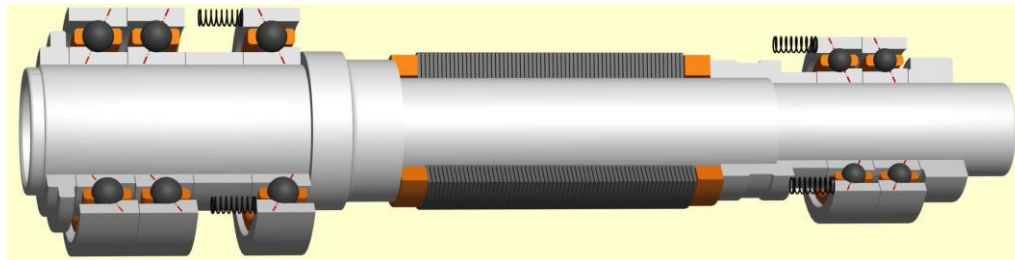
Компоновка шпиндельного вузла з трьома підшипниками в передній опорі
